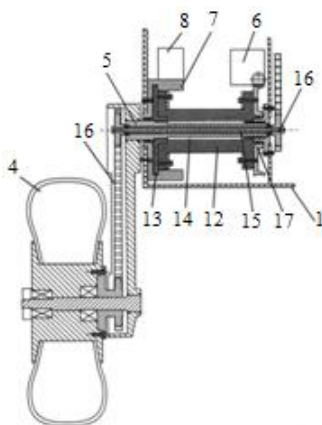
Пристрій підвіски: 1 – рама або корпус; 4 – колесо; 5 – вал; 6 – привід повороту; 7 – засіб блокування; 8 – електропривод; 12 – полімерна торсіонна втулка; 13 – з'єднувальний диск або зубчасте колесо; 14 – осьовий канал; 15 – передавальний вал; 16 – зубчаста або ланцюгова передача; 17 – черв'ячне колесо
